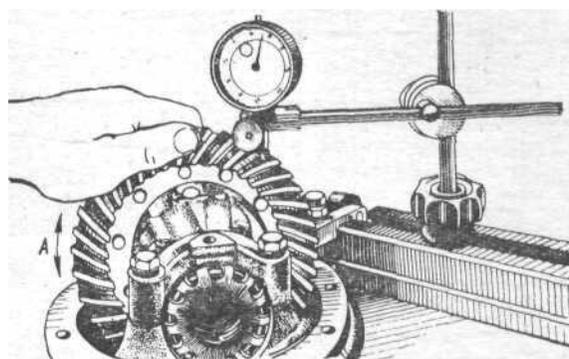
Проверка бокового зазора в зацеплении зубьев шестерен главной передачи индикатором
